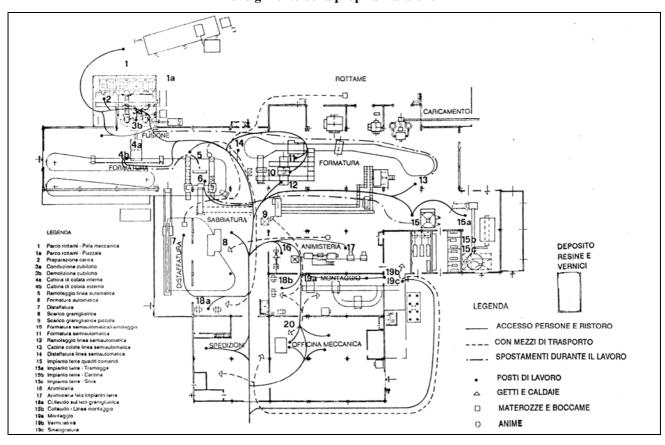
Fonderia di ghisa. Individuazione delle aree di lavoro, disposizione degli impianti e dei depositi
